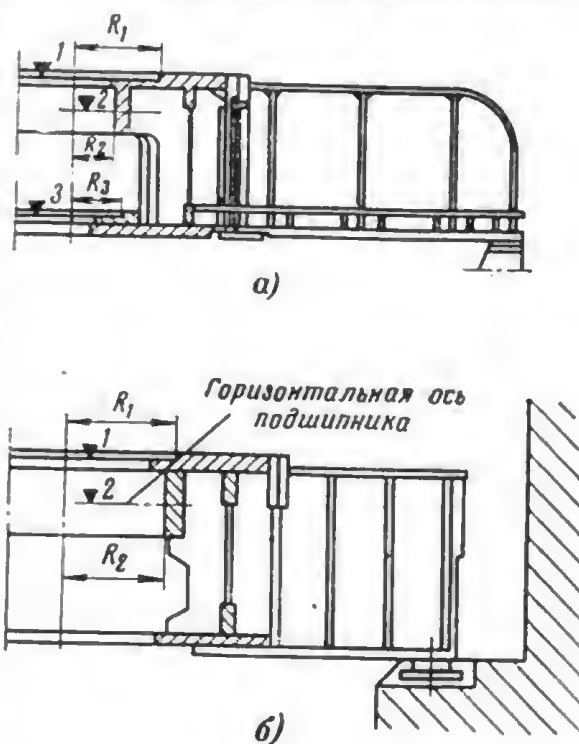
Схема установки и проверки верхней и нижней крестовин генератора.
